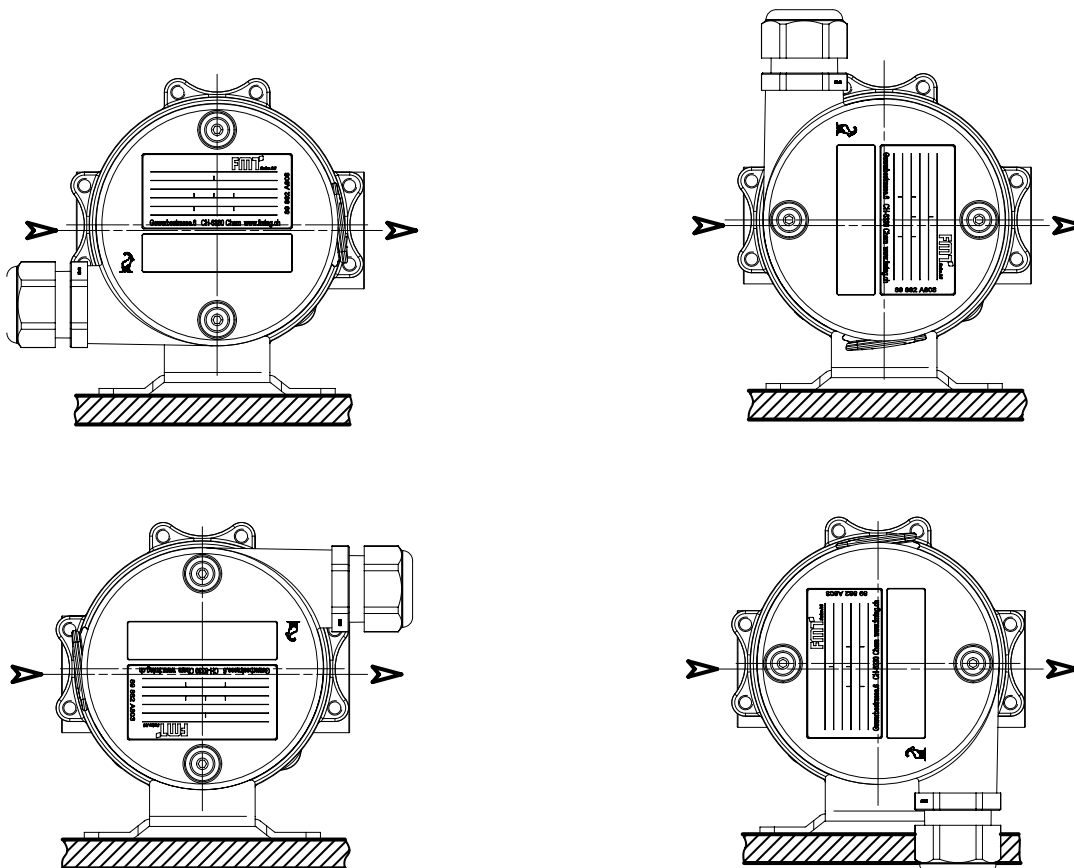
Possibile montaggio del coperchio dell'interruttore
